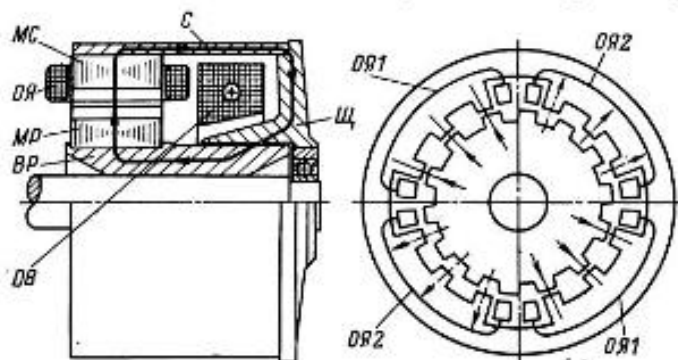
Продольный разрез редукторного двигателя с осевым подмагничиванием
